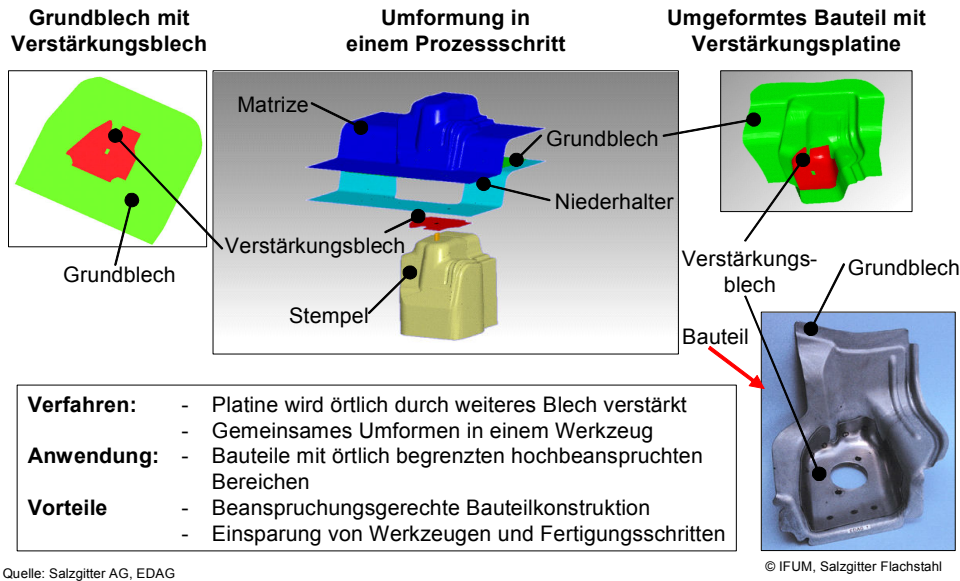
Aufbau eines Werkzeugs zum gemeinsamen Umformen von Grund- und Verstärkungsblech in der Patchwork oder Bonded Blank Technik
